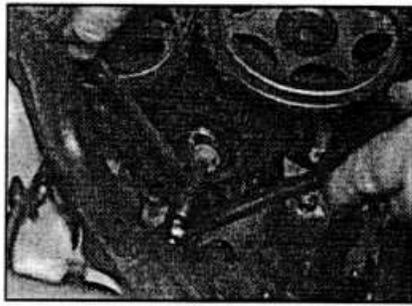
С.14. Ослабление центрального болта механизма натяжения, и использование ключа, для поворота механизм натяжения от зубчатого ремня.
